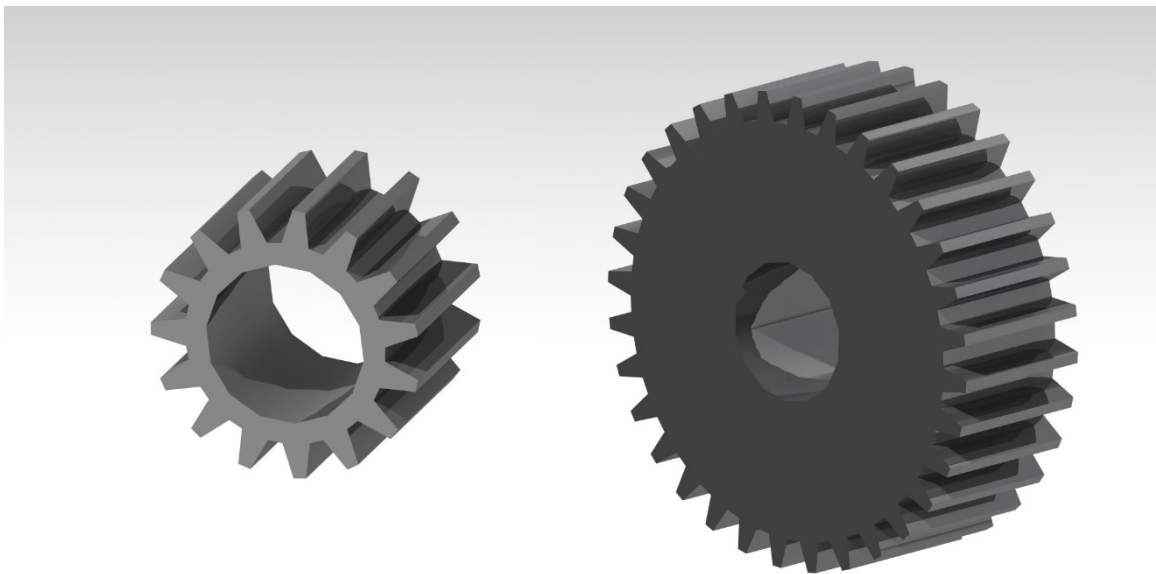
Engrenagem 1 (esquerda) e engrenagem 2 (direita). Fonte: Autor.
